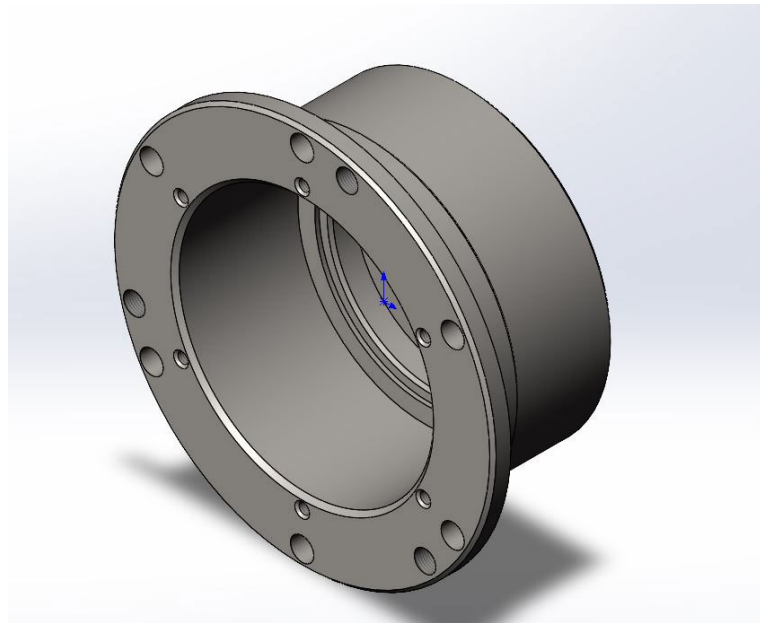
3D модель деталі «Корпус підшипника»
